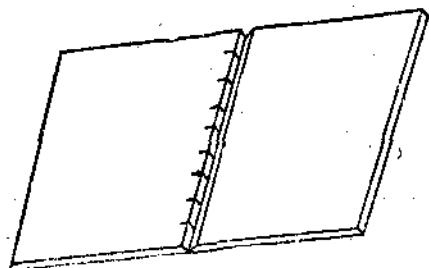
Подготовка к сварке просечкой и скашиванием.
